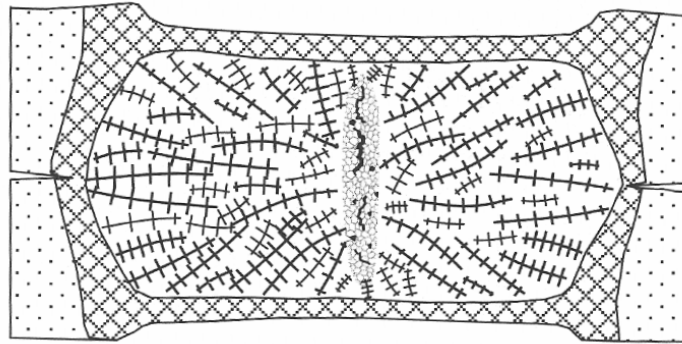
24. Estructura esquemática de un punto de soldadura con enfriamiento rápido a través del metal base y deficiente en los electrodos.<sup>24</sup>
